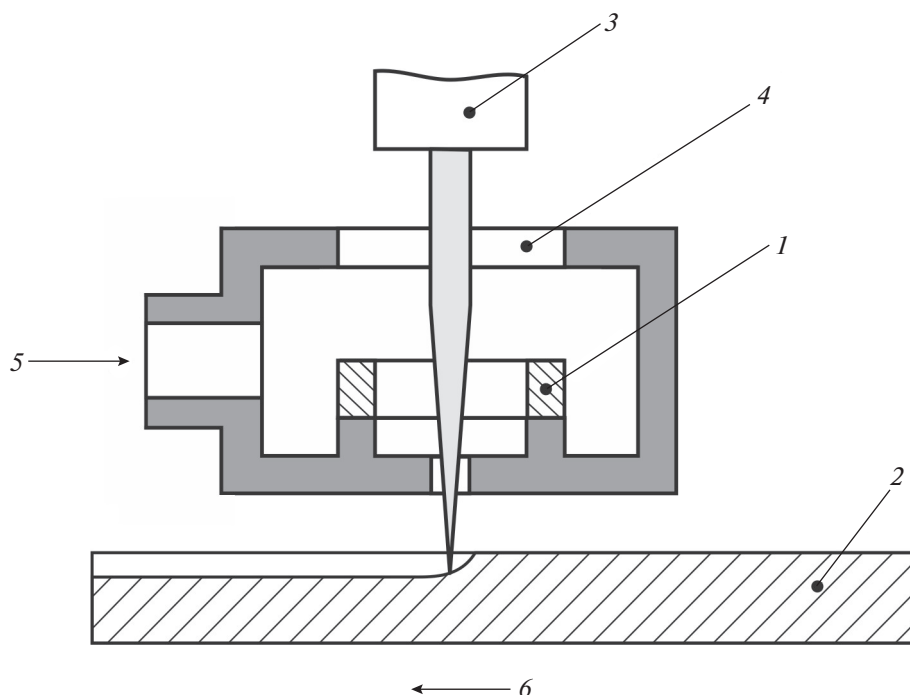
Схема ЛЭХО: 1 – катод, 2 – обрабатываемая деталь, 3 – лазер, 4 – фокусирующее устройство, 5 – вход электролита, 6 – направление движения обрабатываемой детали при травлении “дорожки”.
